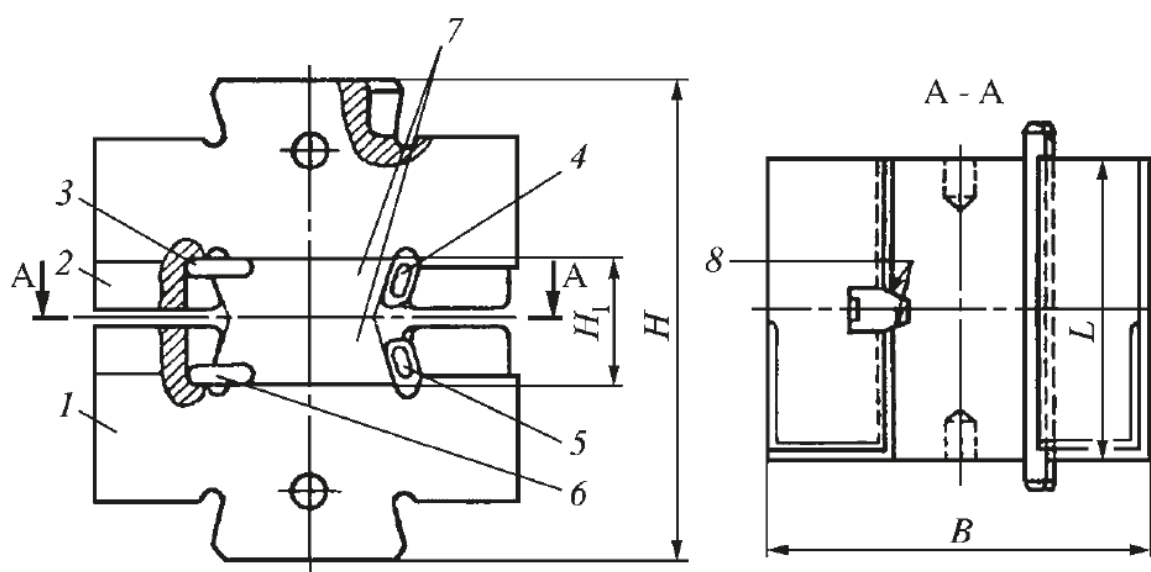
Блоки универсальные молотовых штампов с призматическими вставками [2]: 1 — нижний блок; 2 — верхний блок; 3 — верхняя шпонка; 4 — верхний клин; 5 — нижний клин; 6 — нижняя шпонка; 7 — призматические вставки
